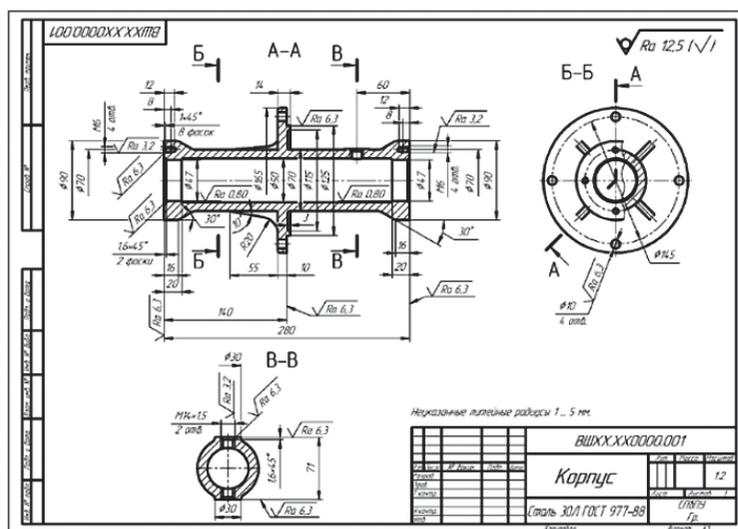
Чертеж корпуса, подлежащего замене на сварную сборочную единицу
